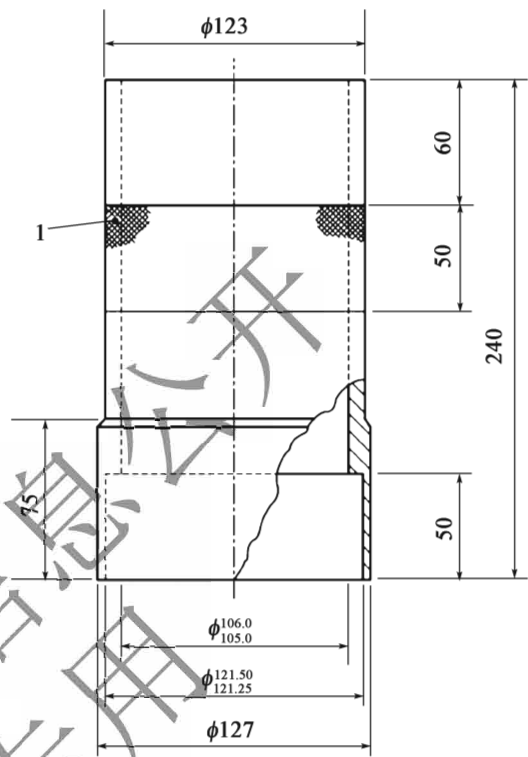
挤压筒示意图 (尺寸单位: mm)
